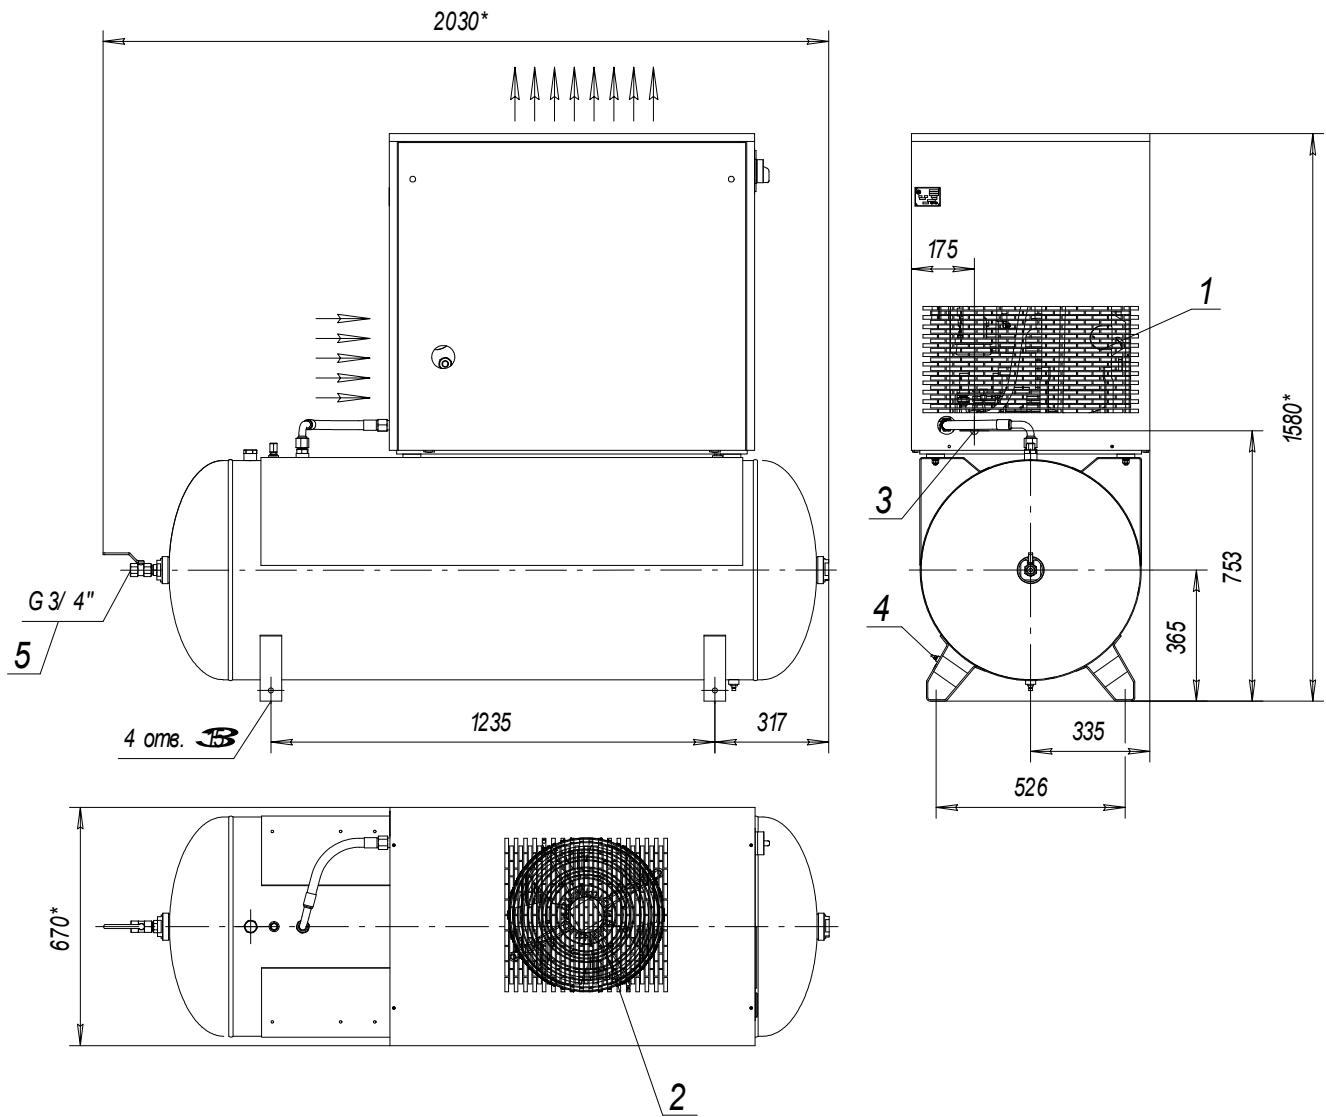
Общий вид компрессорной установки ВК20Е-8(10, 15)-500
